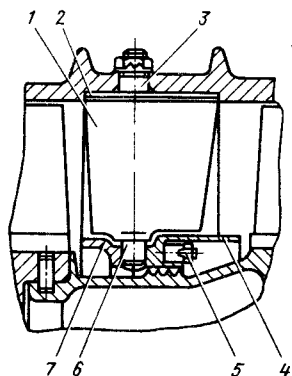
Разборный направляющий аппарат с жестким креплением к корпусу
